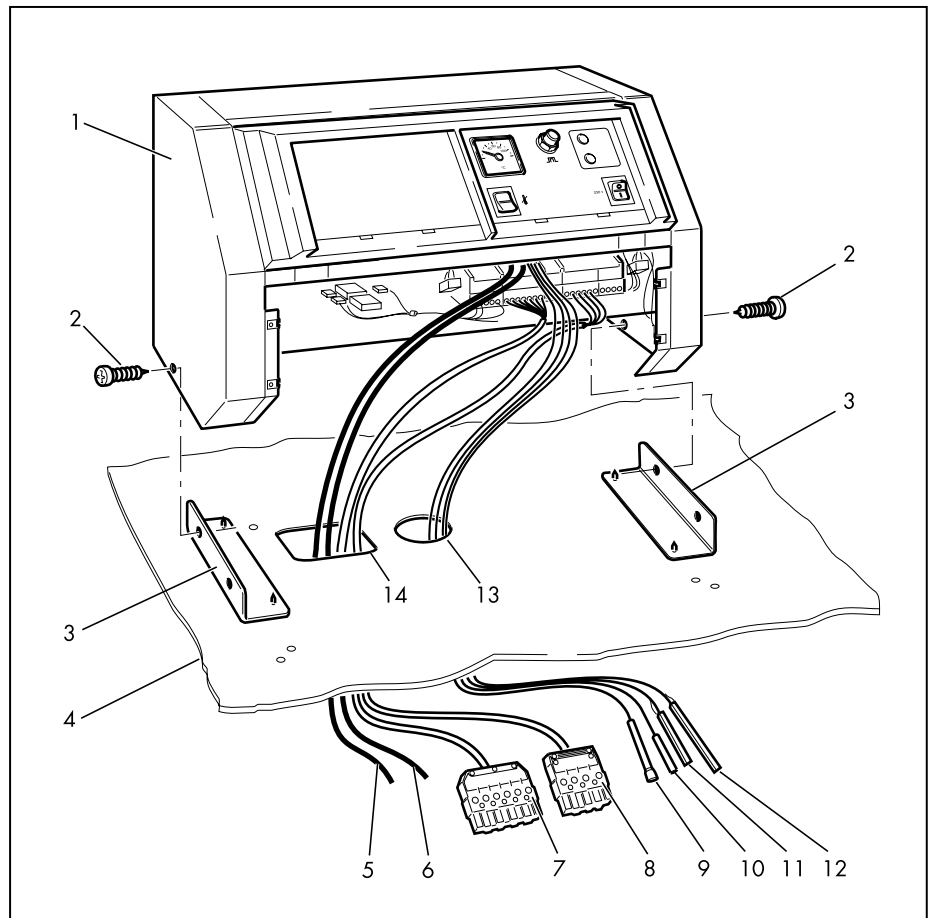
Befestigung des Kessel-Schaltpultes (Im Beispiel VKB...)
